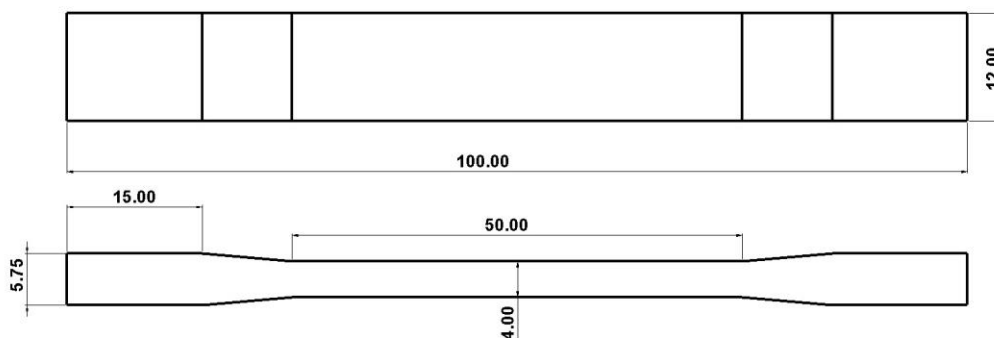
Géométrie de l'éprouvette de traction (dimensions en millimètre).
